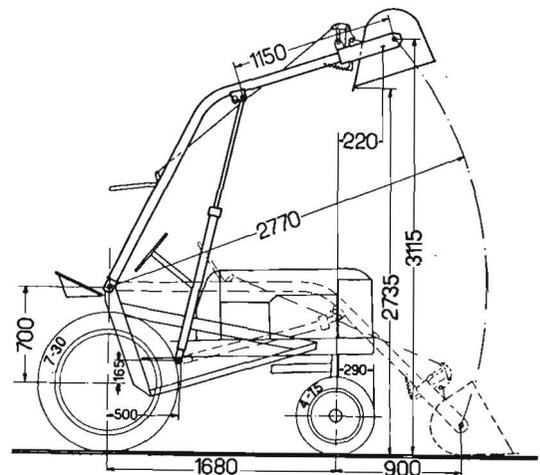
Earthmaster mit Lader. Hubweg der Schaufel 2875 mm; Hubweg des Kolbens 775 mm; Durchmesser des Kolbens 38 mm
